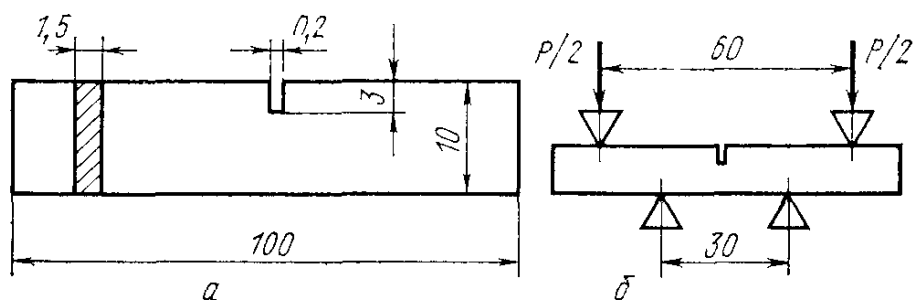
Образец (а) и схема нагружения (б) при испытании на замедленное разрушение по методу ЛТПЗ
